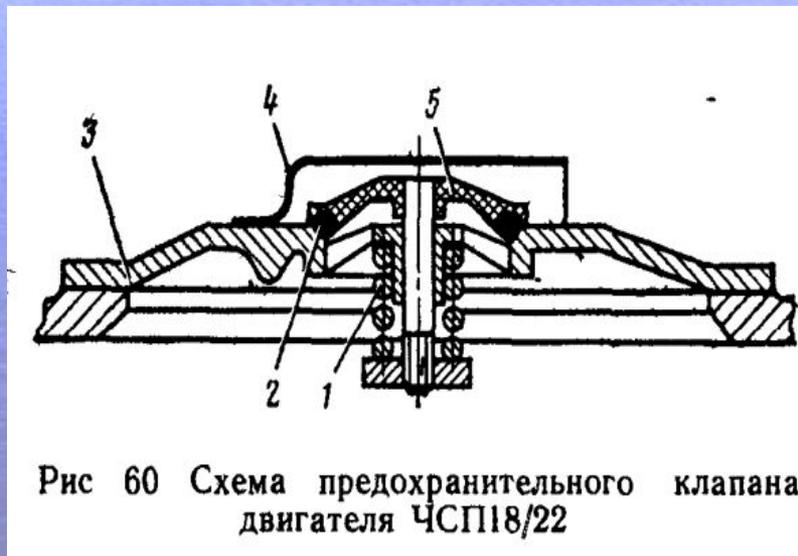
Схема предохранительного клапана двигателя ЧСП18/22
